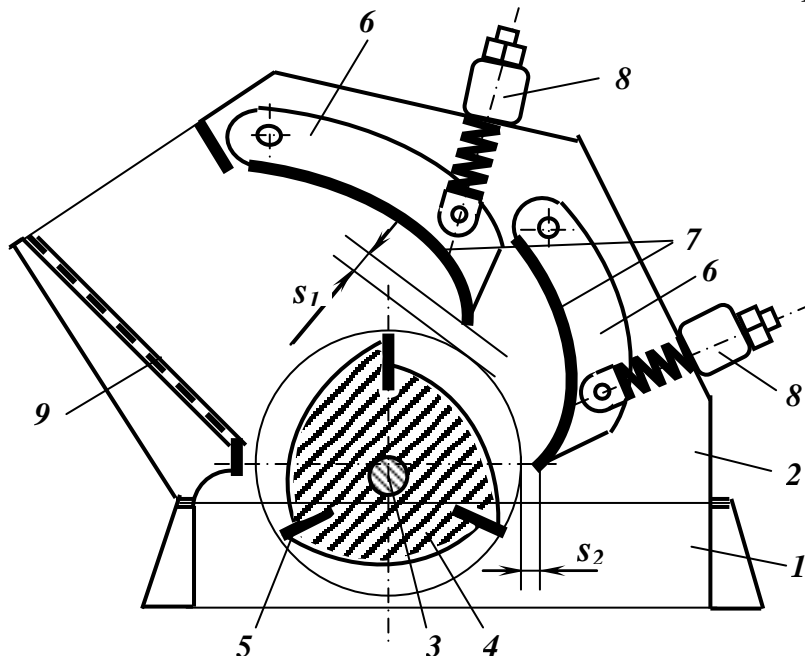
Однороторна дробарка крупного дроблення.
